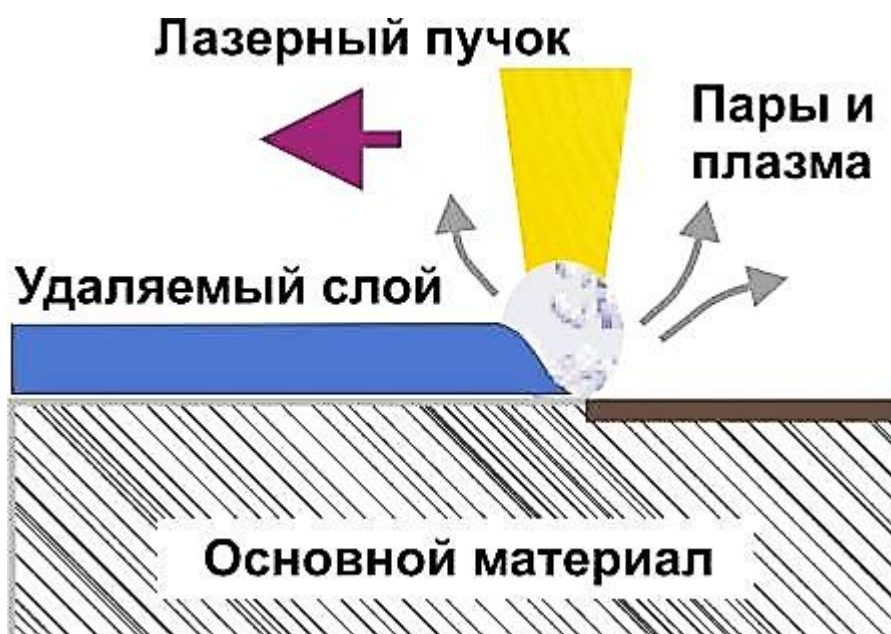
Принципиальная схема процесса лазерной очистки поверхности алюминиевых сплавов перед сваркой
